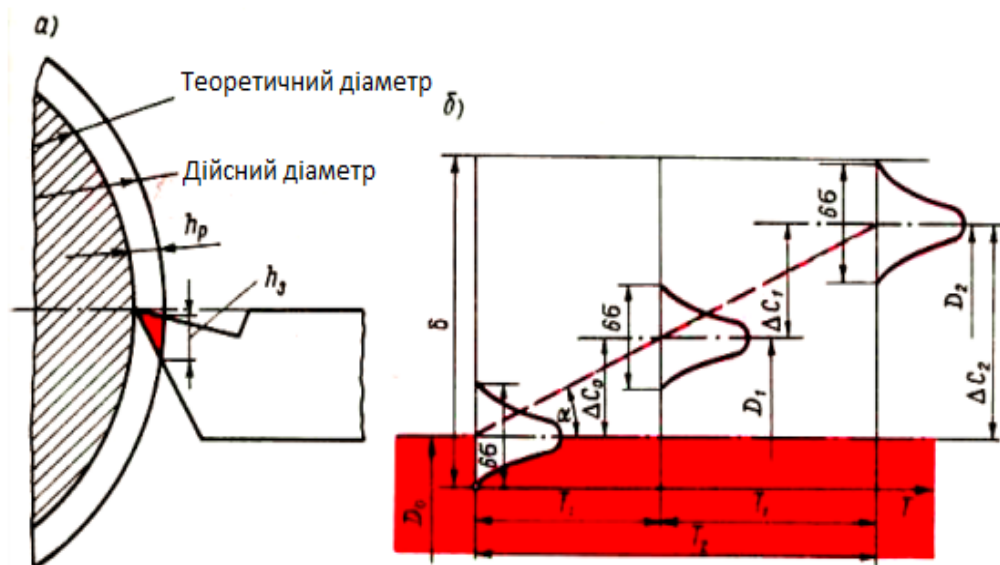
Схема спрацювання металообробного інструменту: а) відхилення розмірів деталі; б) зміщення поля розкиду розмірів деталі.
